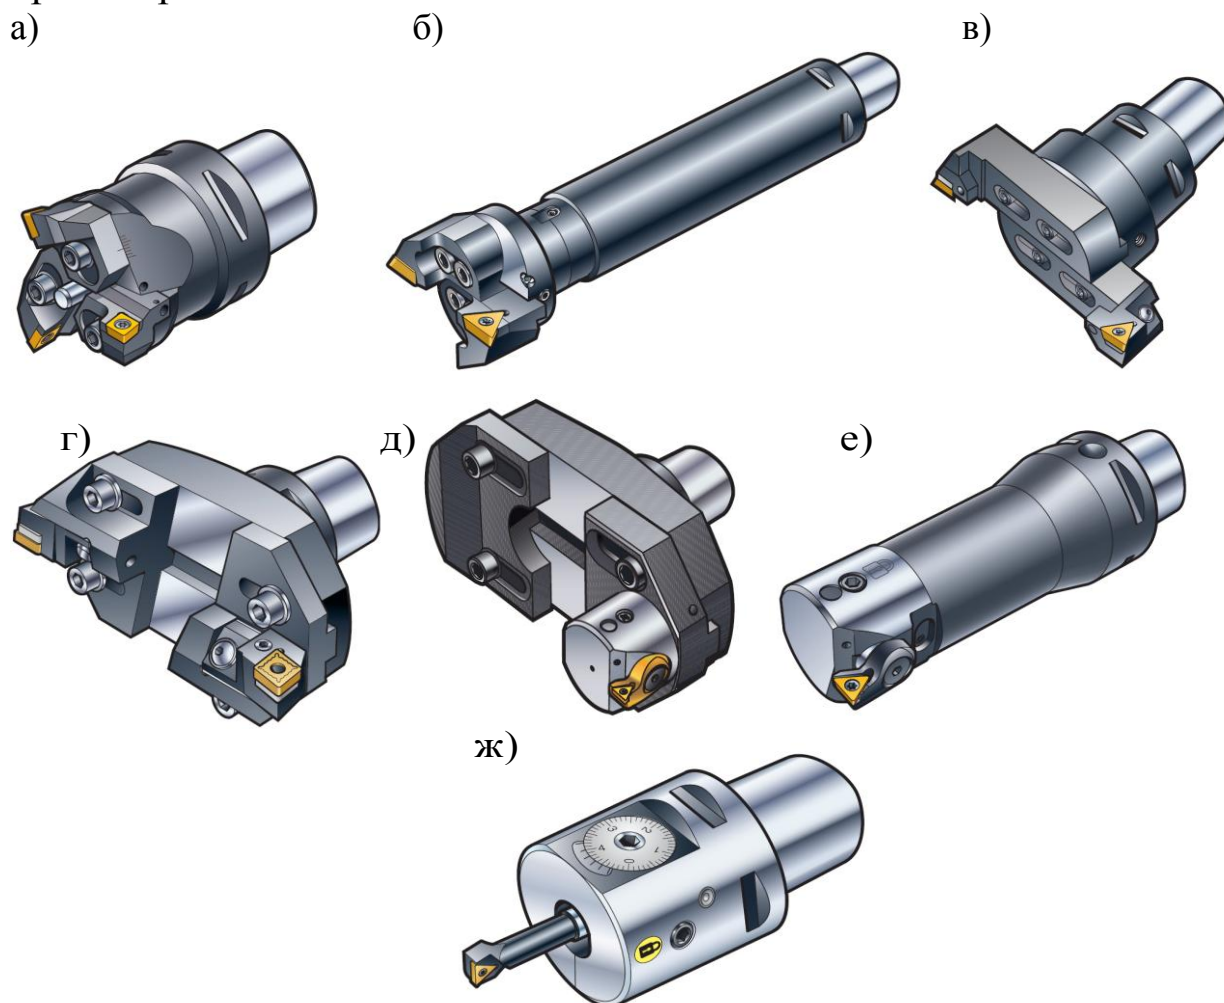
Конструктивное исполнение расточных оправок: а, б, в, г – трех- и двухрезцовые оправки для чернового растачивания; д, е, ж – однорезцовые оправки для чистового растачивания
